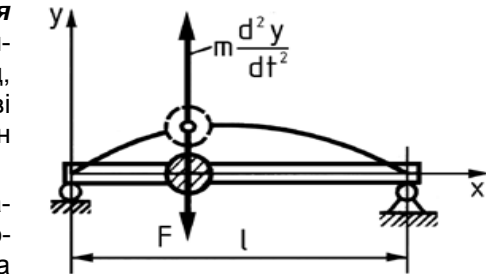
Розрахункова схема згинальних коливань однасової системи деталей вала
